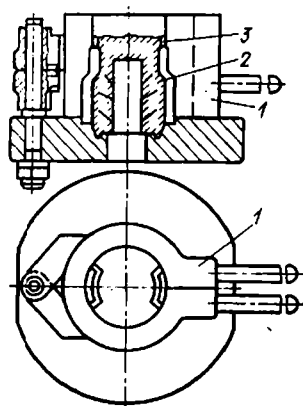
Кокиль для пустотелой гайки из ковкого чугуна: 1 — кокиль; 2 — песчаный стержень; 3 — дождевые питатели
